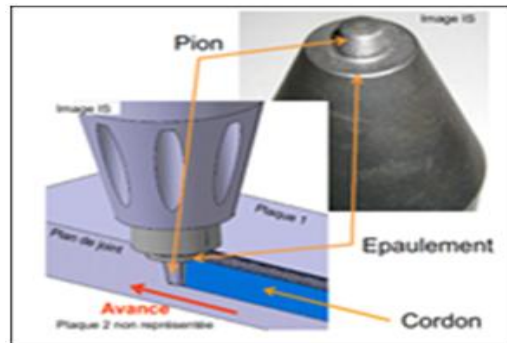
Forme d'outil pour le soudage FSW [34].
